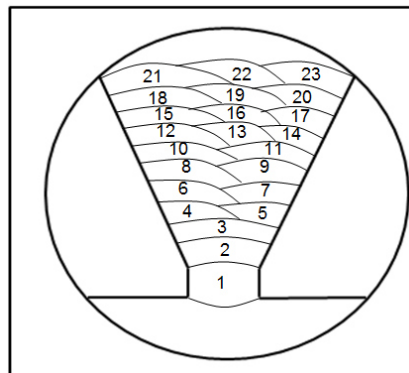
Secuencia de deposición de los cordones de soldadura.
